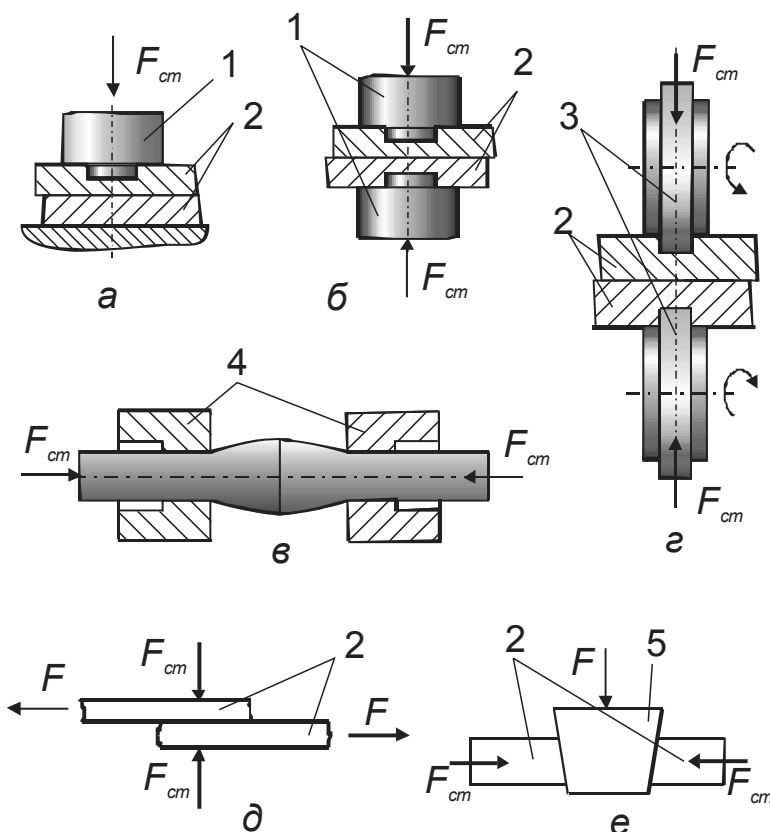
Схеми холодного зварювання: а - точкове з одним пуансоном; б - точкове з двома пуансонами; в - стикове; г - шовне; д, е - зсувом; 1- пуансони; 2 - деталі, що зварюють; 3 - ролики; 4 - затискачі; 5 - клин
